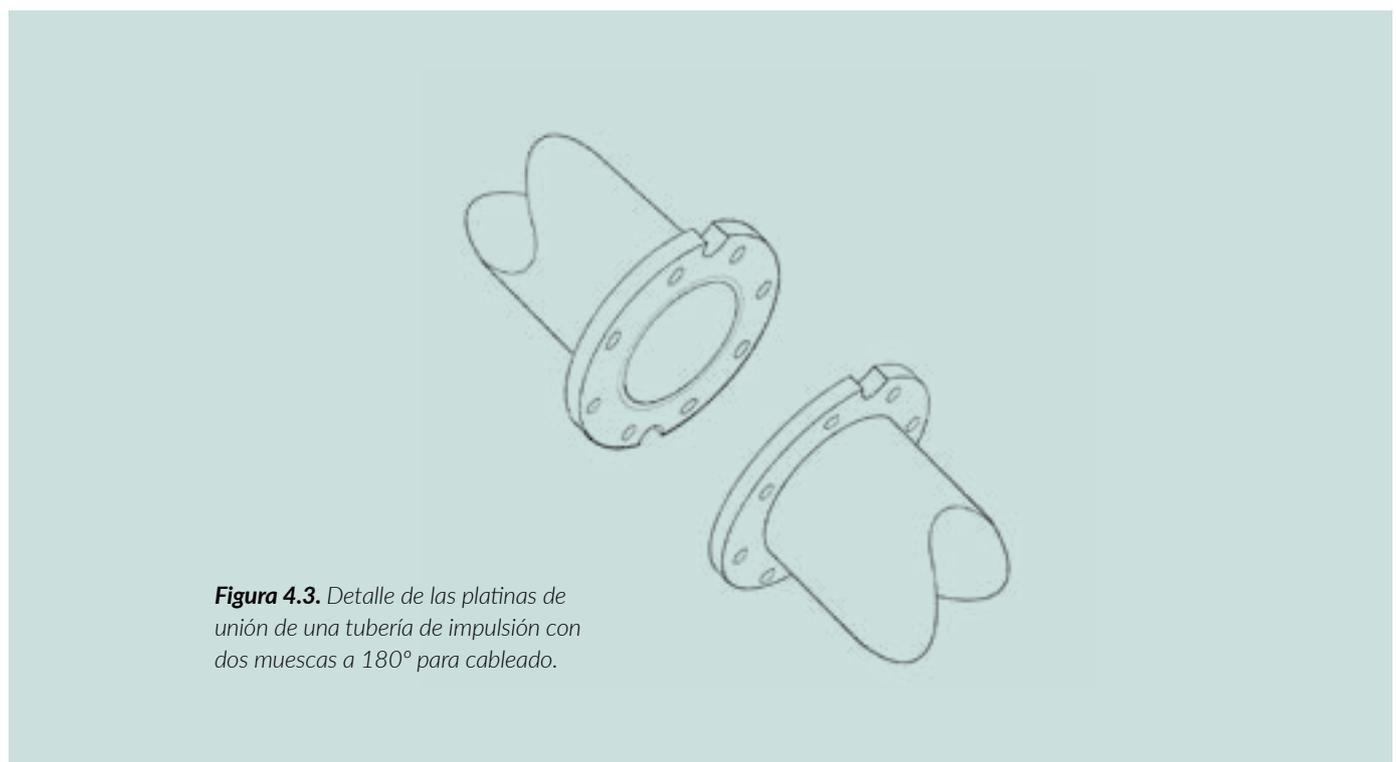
Detalle de las platinas de unión de una tubería de impulsión con dos muescas a 180° para cableado.
